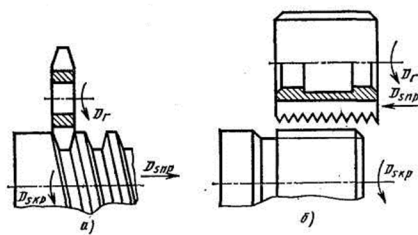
Схемы фрезерования наружной резьбы фрезой:
